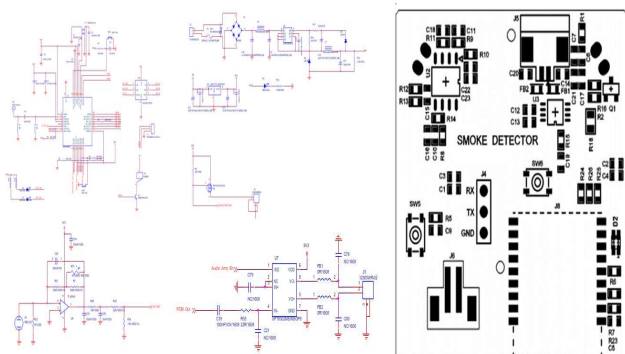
일산화탄소 감지 회로도(좌) 및 연기감지 PCB 도면(우)
